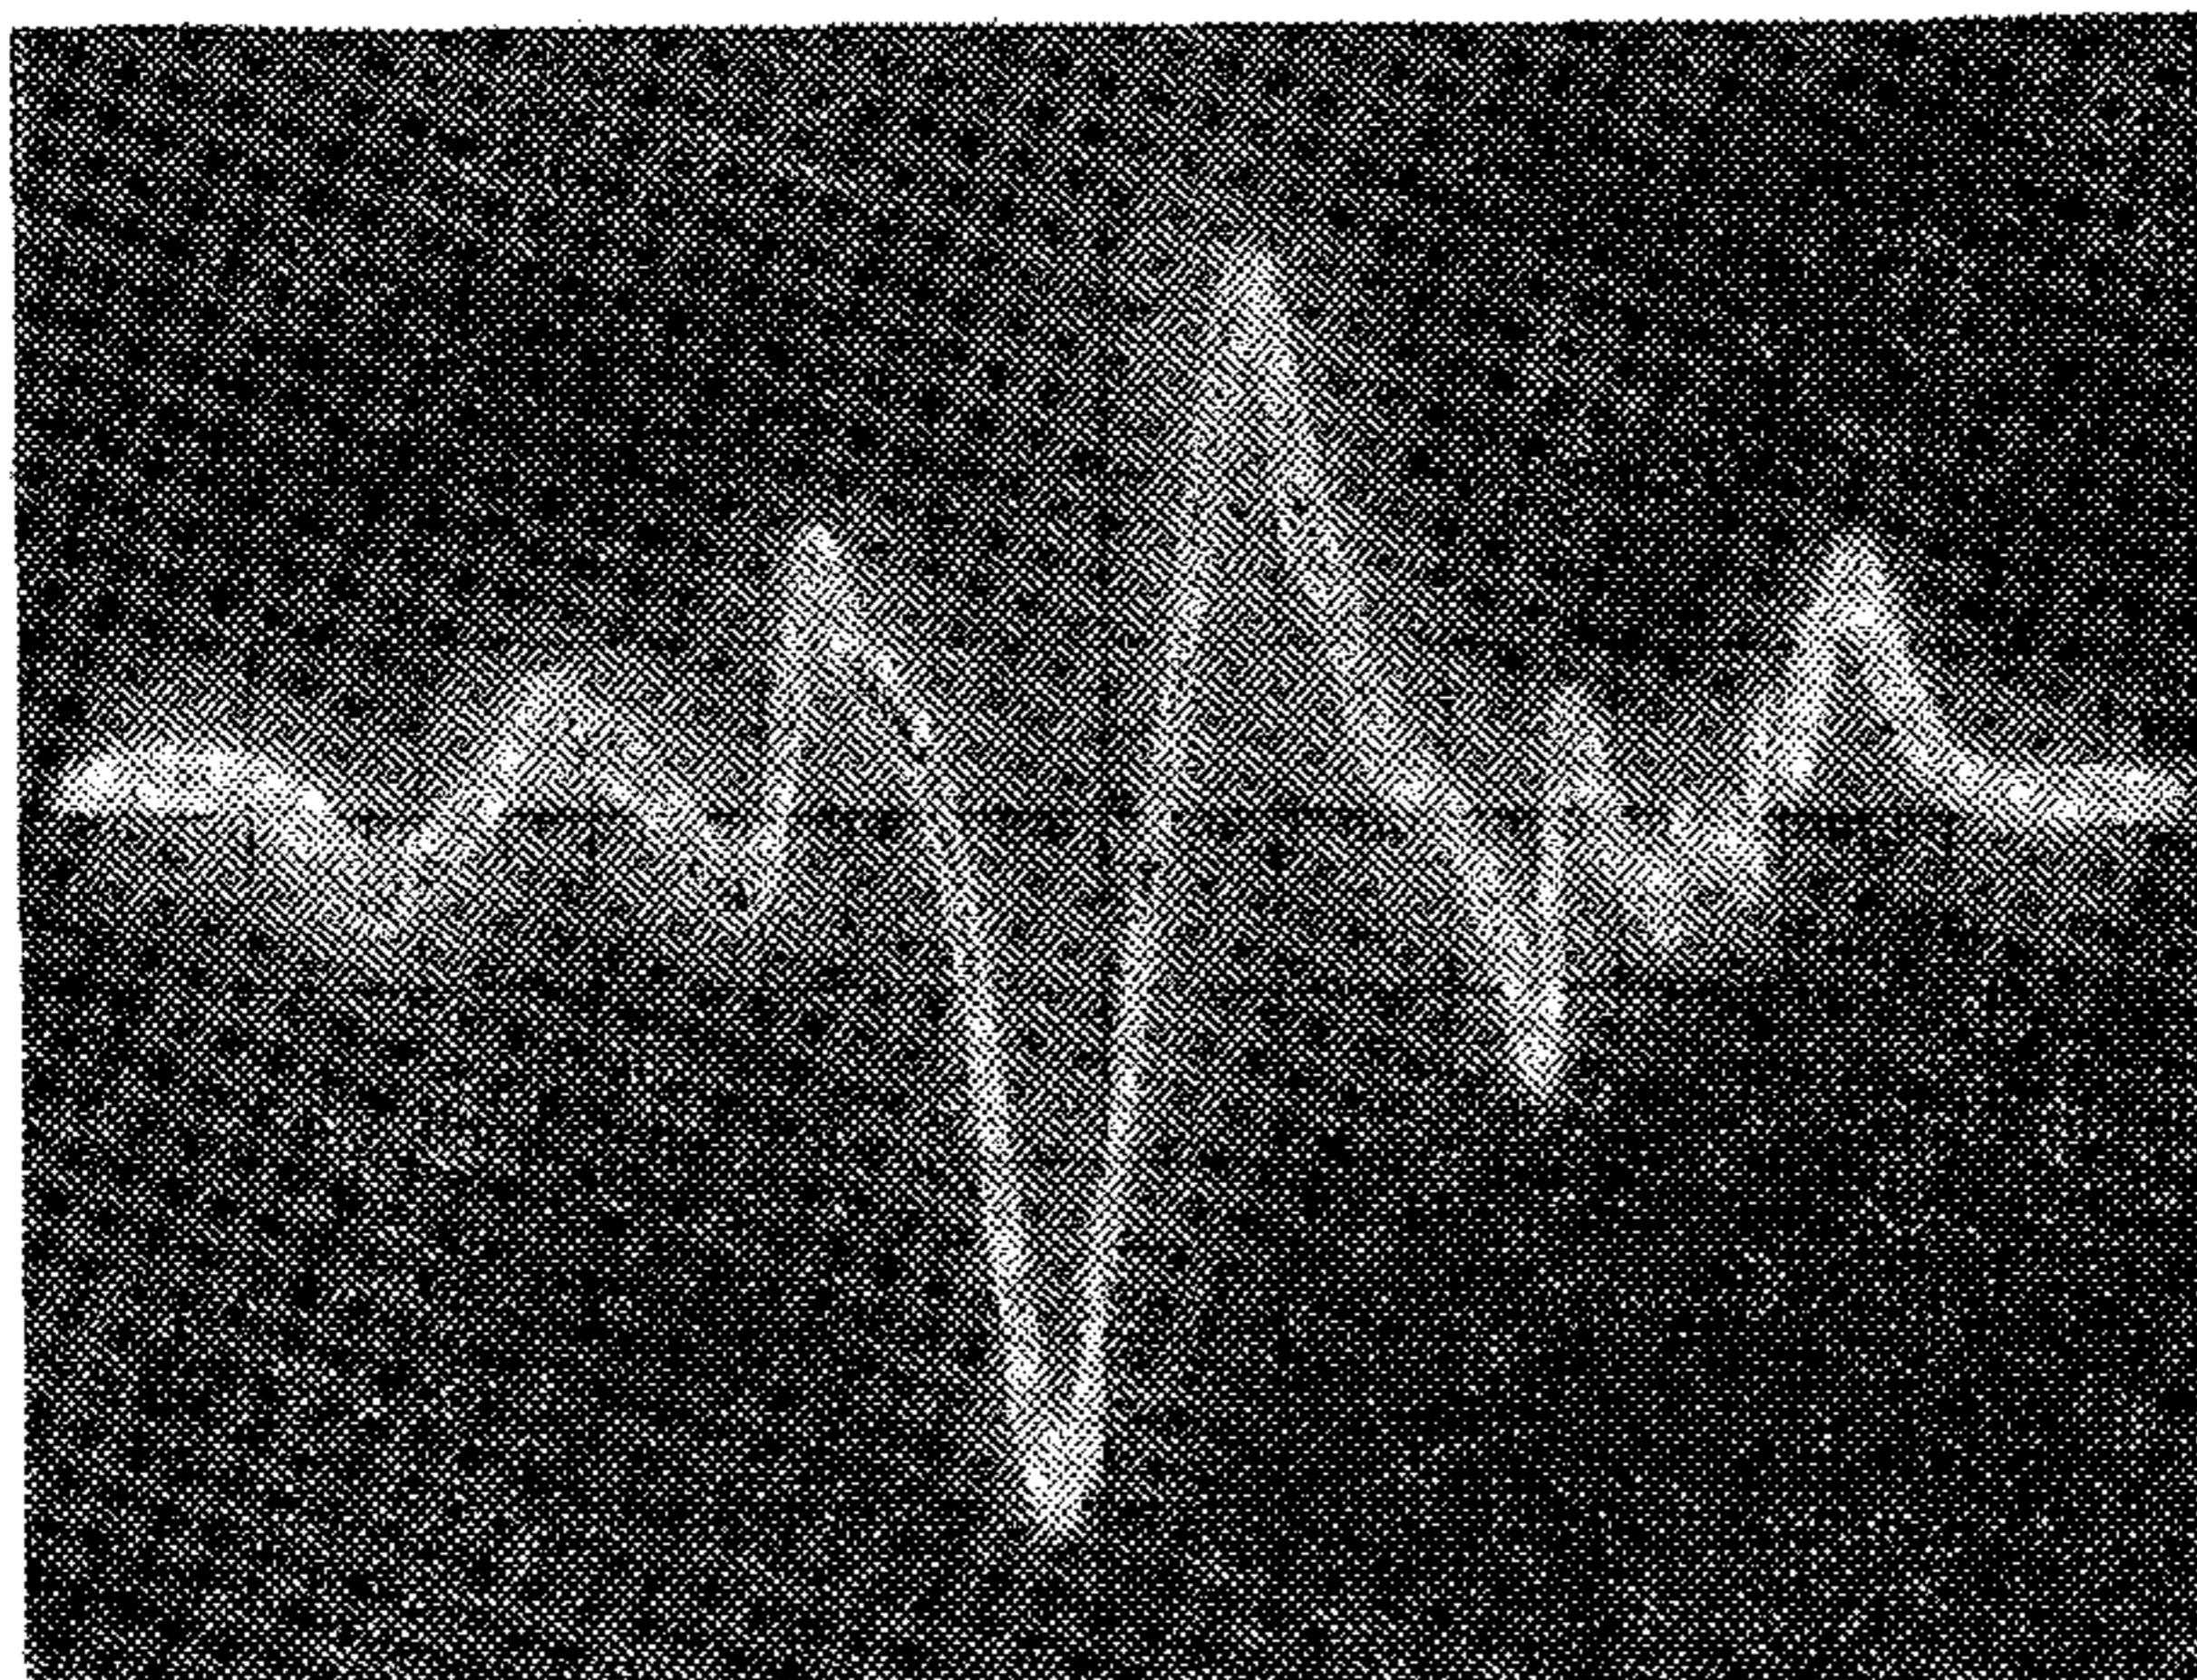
Изображение импульсов от участка сварного шва с непроваром
